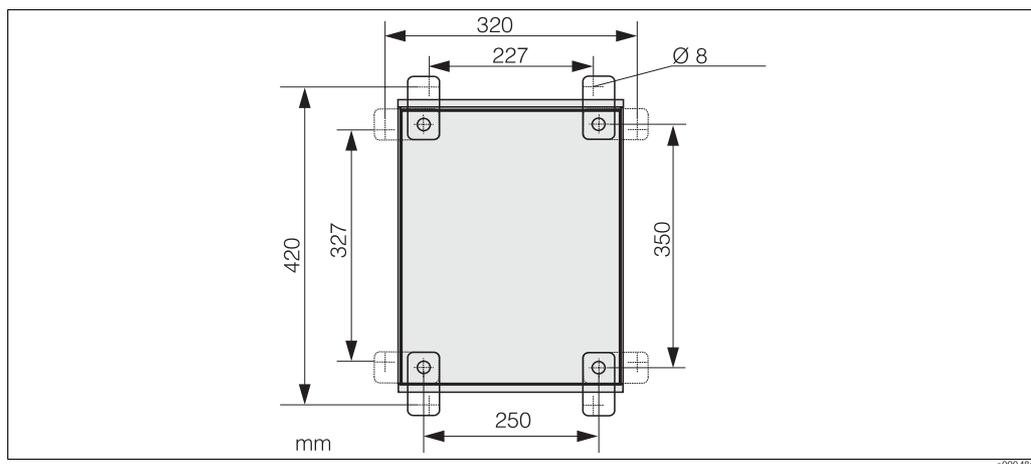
Dimensioni per il montaggio a parete utilizzando il relativo kit di montaggio (incluso nella fornitura)
